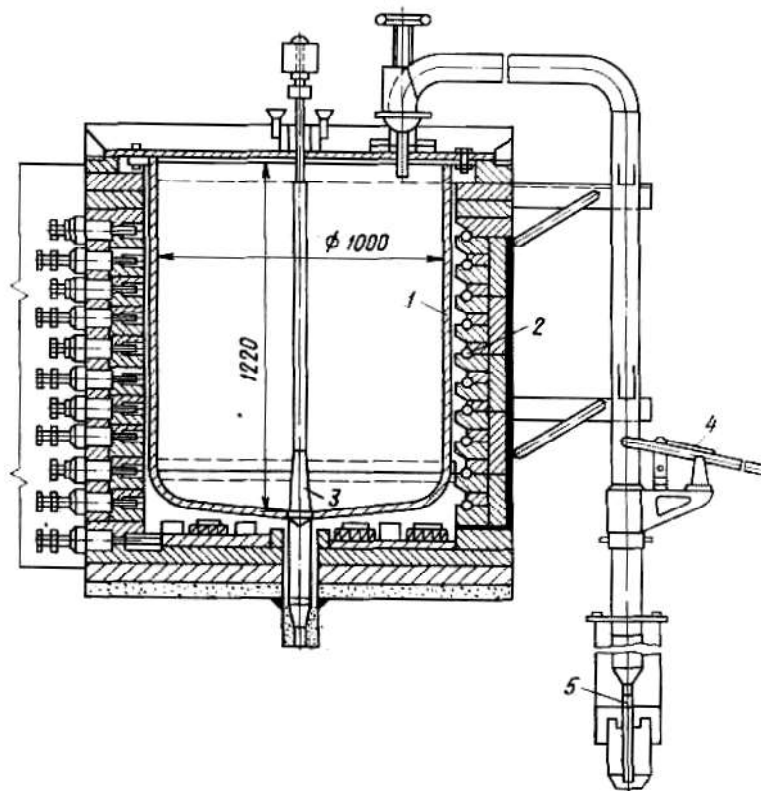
Вакуум-ковш для извлечения магния: 1 – тигель; 2 – нагреватель; 3 – запорный клапан; 4 – шланговый запорный клапан; 5 – заборное устройство
